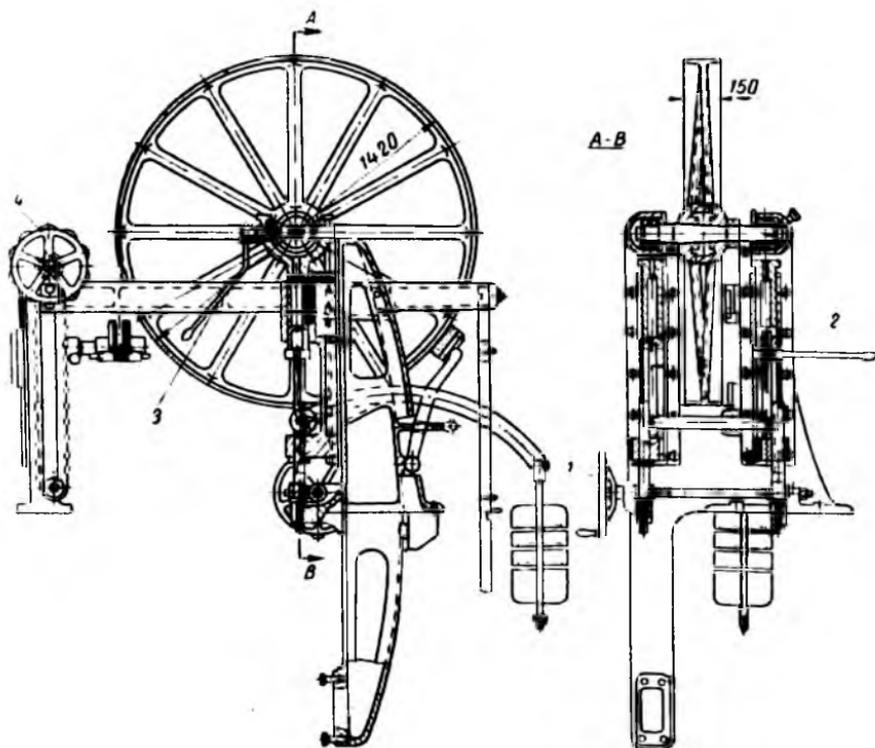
Верхний пильный шкив ленточнопильного ребрового станка:
